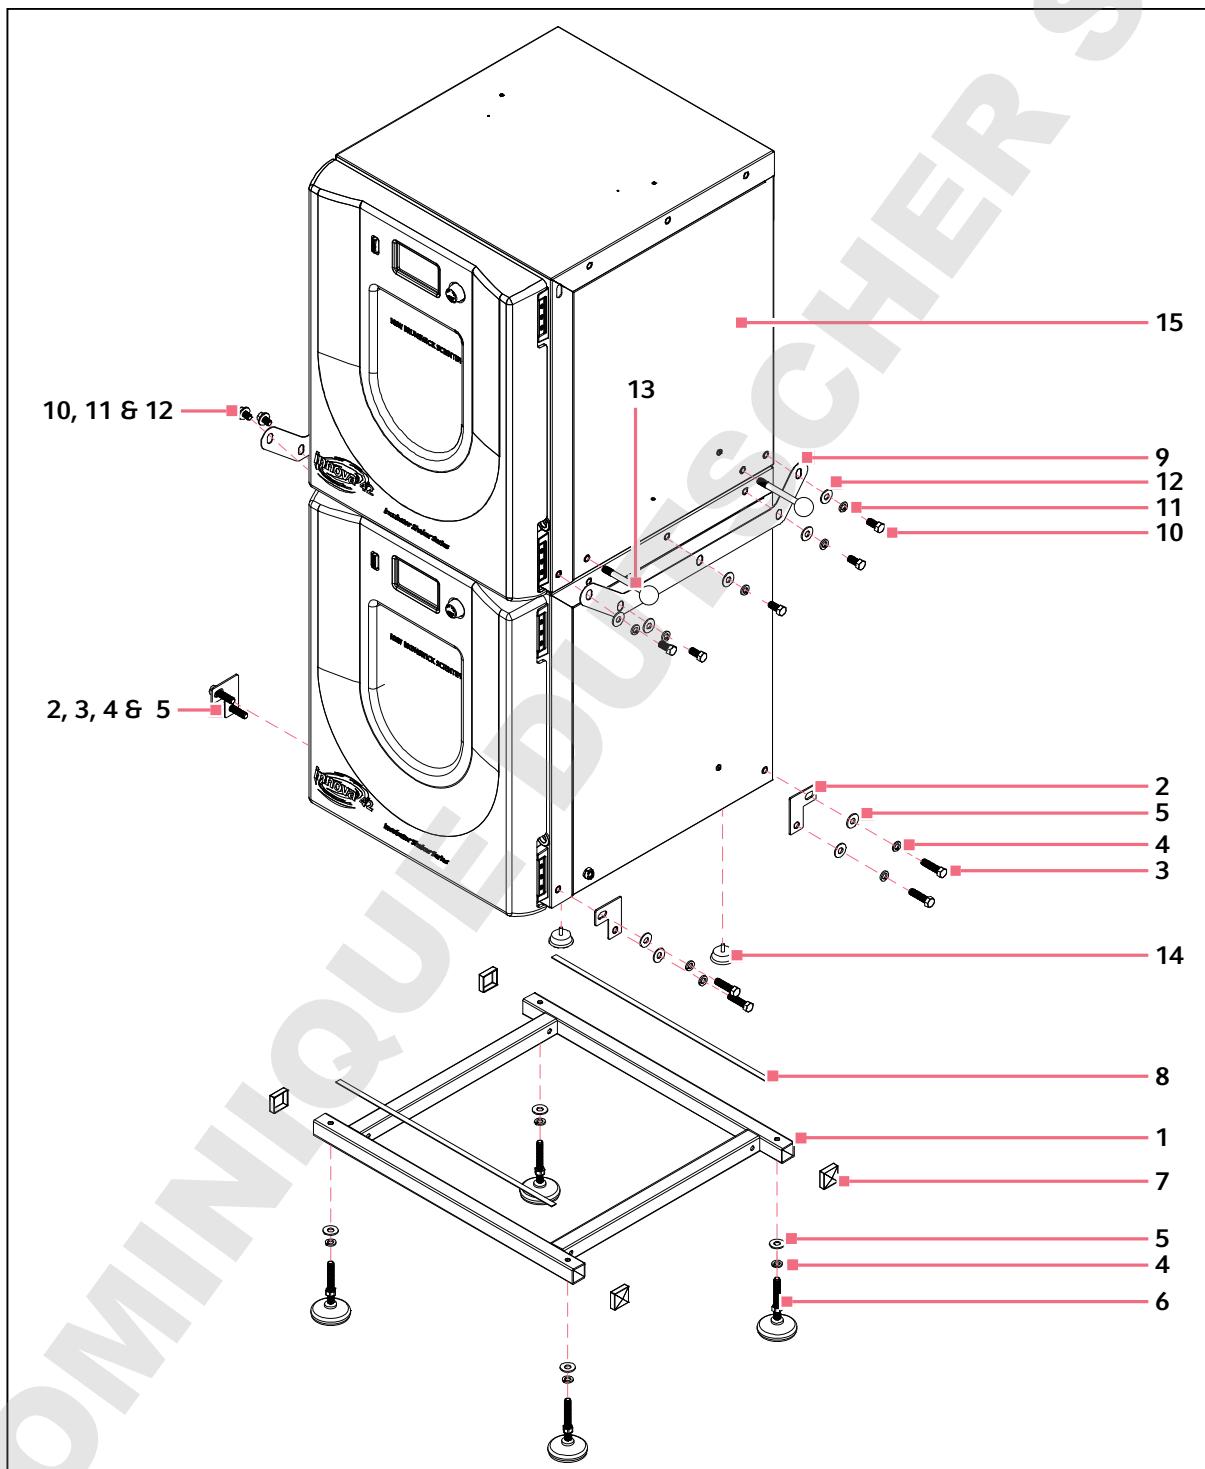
Pièces du kit de superposition (vue éclatée)
